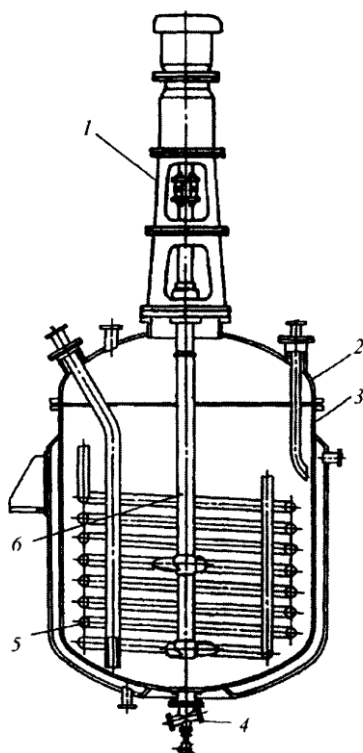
Реактор повного перемішування: 1 – привод; 2 – кришка; 3 – корпус; 4 – зливальний клапан; 5 – змійовик; 6 – вал із мішалками
